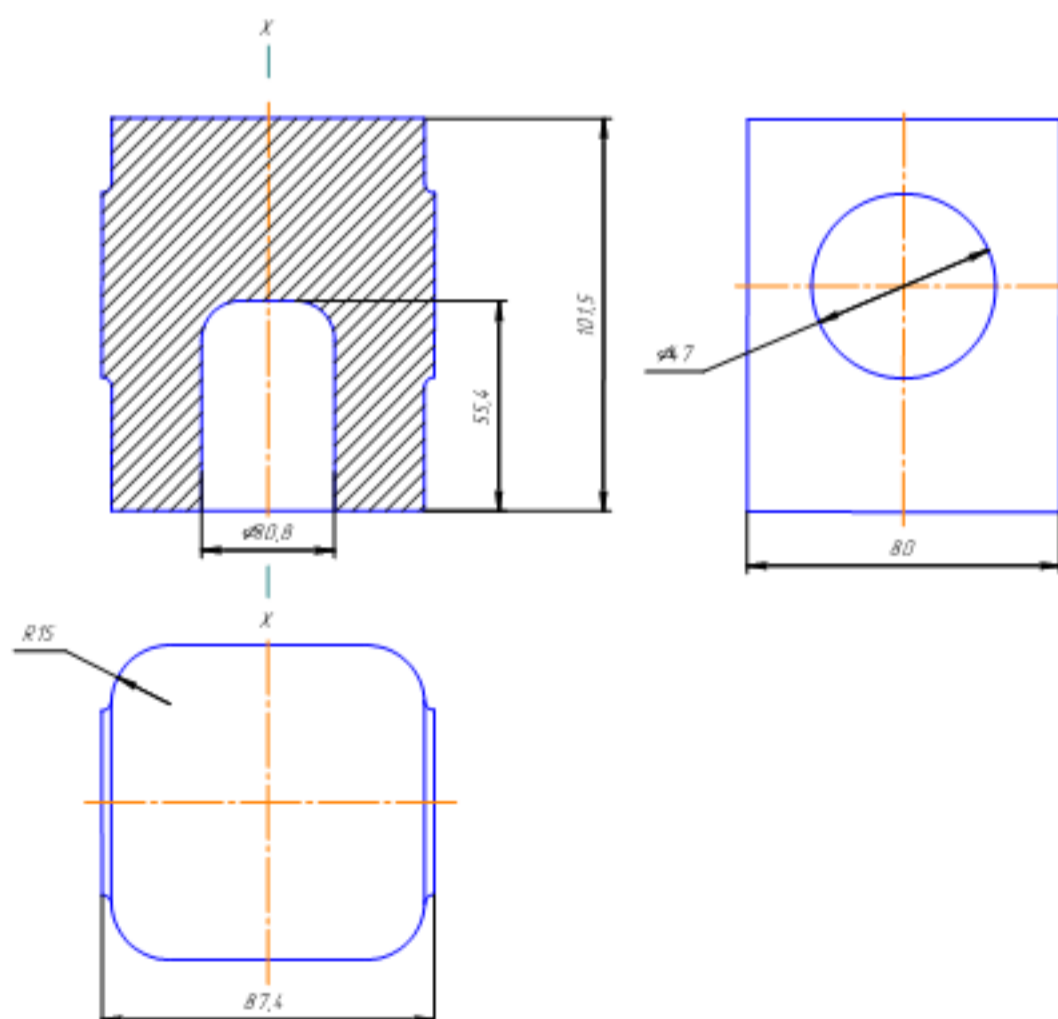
Ескіз заготовки одержаної литтям в кокіль
